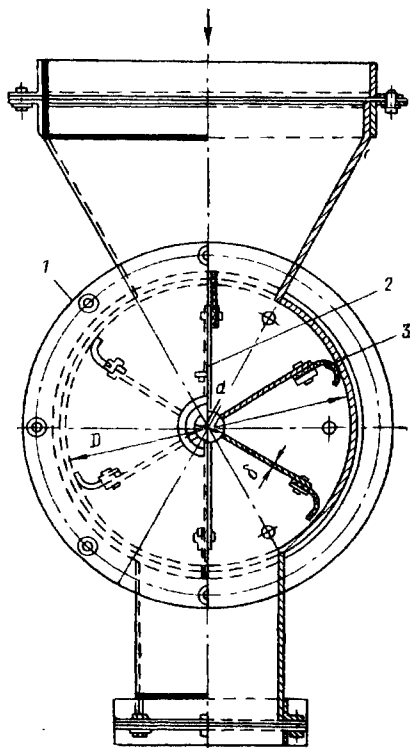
Шлюзовый питатель барабанного типа с гибкими наконечниками на лопастях ротора конструкции Гипродрева
